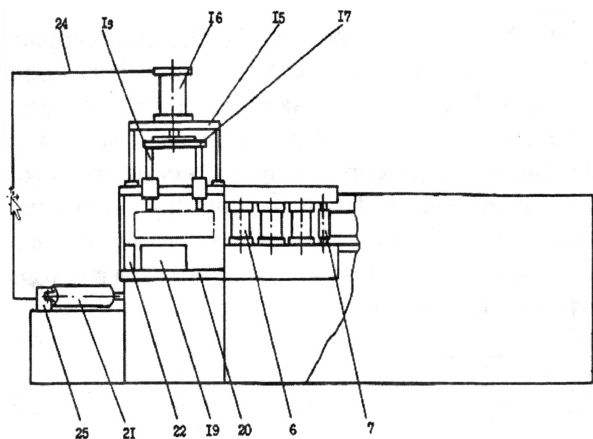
Схема стана для прокатки заготовок малолистовых рессор
